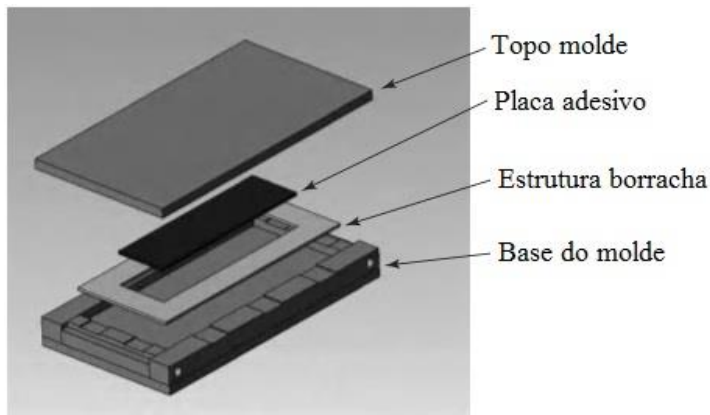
Vista explodida do molde destinado à produção de placas de adesivo através de pressão hidrostática [20]
